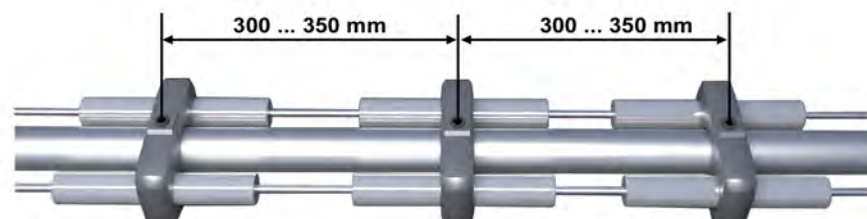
Etape 8 Remplacer les pièces d'usure du brûleur d'allumage
